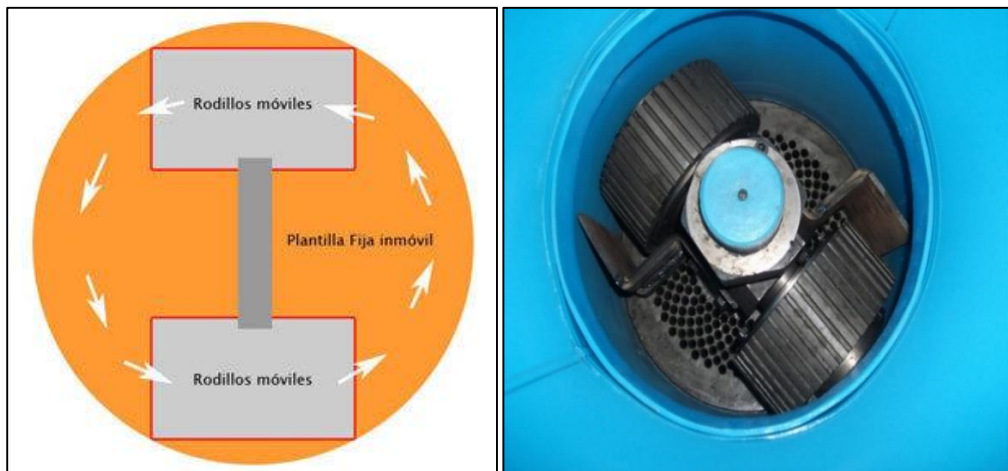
Movimiento del par de rodillos (izq) y conjunto rodillos matriz (der)
